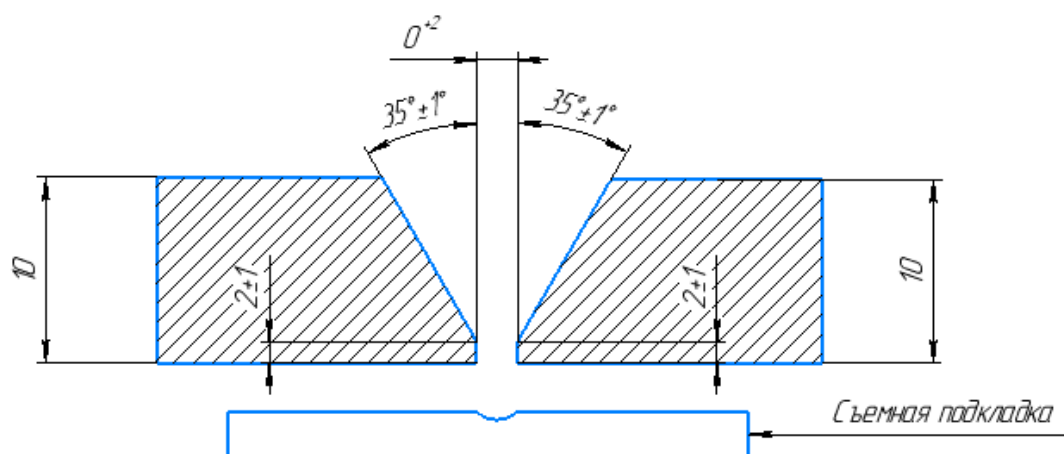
Размеры подготовленных кромок сварных деталей сварного соединения С18 по ГОСТ 14806-80
